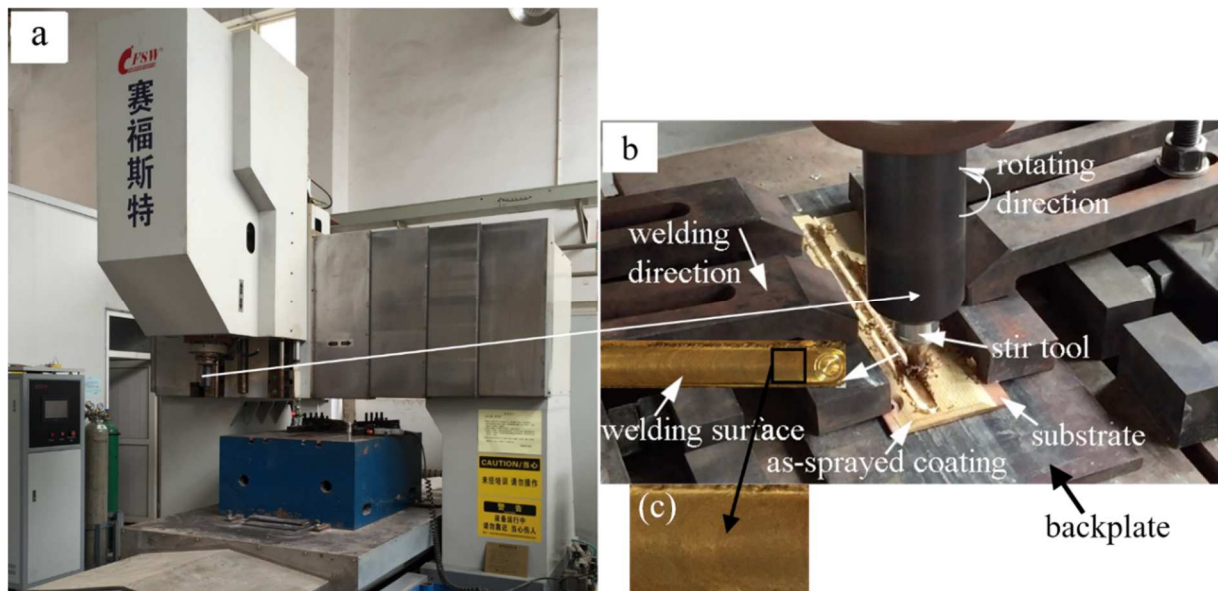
(a) Machine du soudage par friction malaxage et (b) procédé FSP, et (c) morphologie de la soudure générée.
